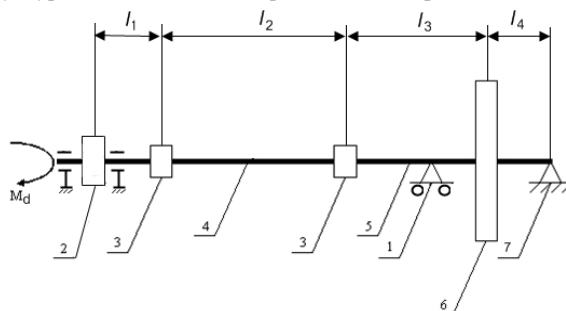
Структурная схема вентиляторного агрегата: 1 – радиальный подшипник; 2 – приводной электродвигатель; 3 – зубчатые муфты; 4 – трансмиссионный вал; 5 – коренной вал ротора; 6 – рабочее колесо; 7 – радиально-упорный подшипник; M_d – крутящий момент электродвигателя
